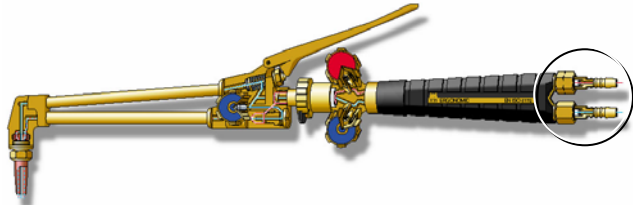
Schweißbrenner mit montierten Rückschlagventilen
